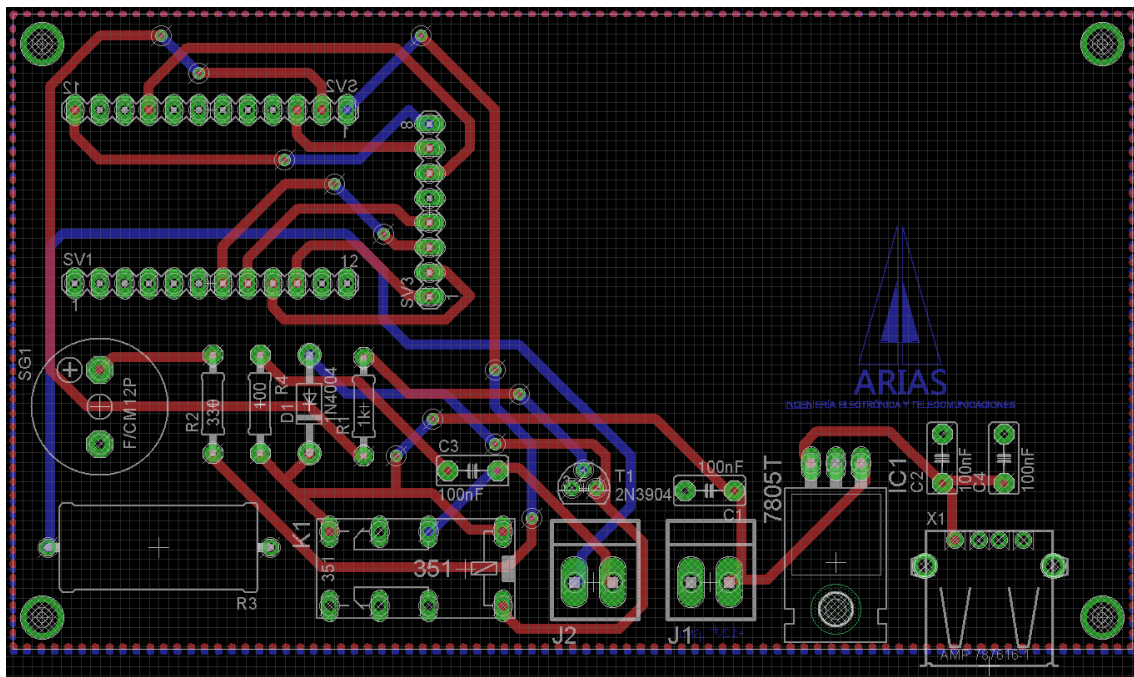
DISEÑO DE CIRCUITO IMPRESO O PCB. FUENTE: EL AUTOR
